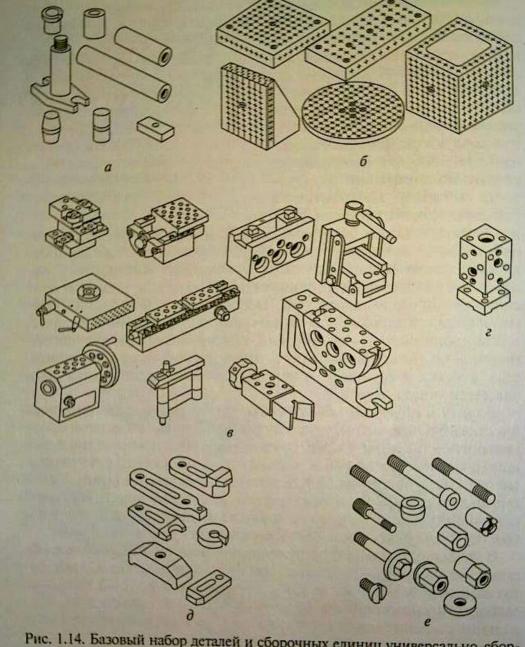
Базовый набор деталей и сборочных единиц универсально-сборных приспособлений:
